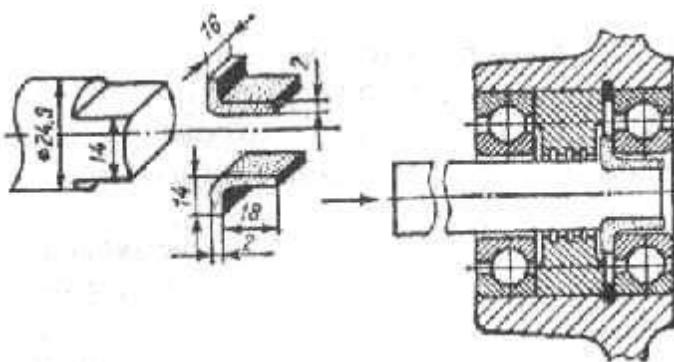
Приспособление для выпрессовки коренных подшипников из картера двигателя, применяемое совместно с универсальным съемником
